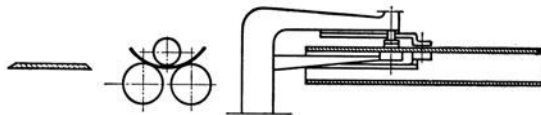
Feuer- bzw. Wassergaspreßschweißung.
